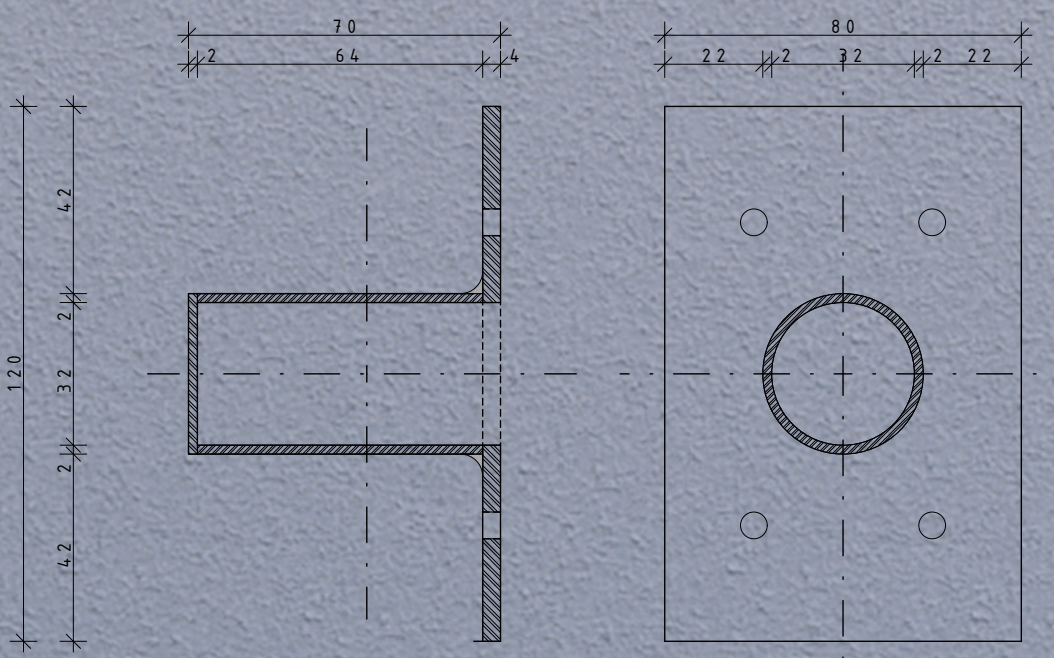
DETAIL DOLNÍHO UCHYCENÍ - M 1:2
